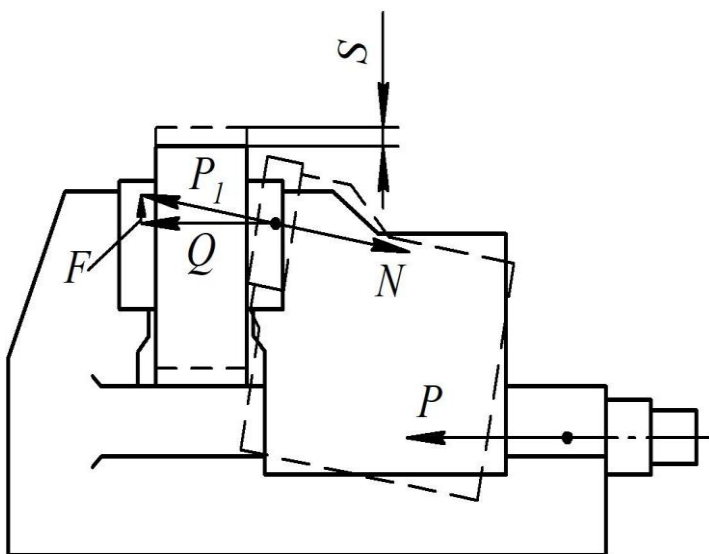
Схема сил, що діють на заготовку під час її закріплення в лещатах
